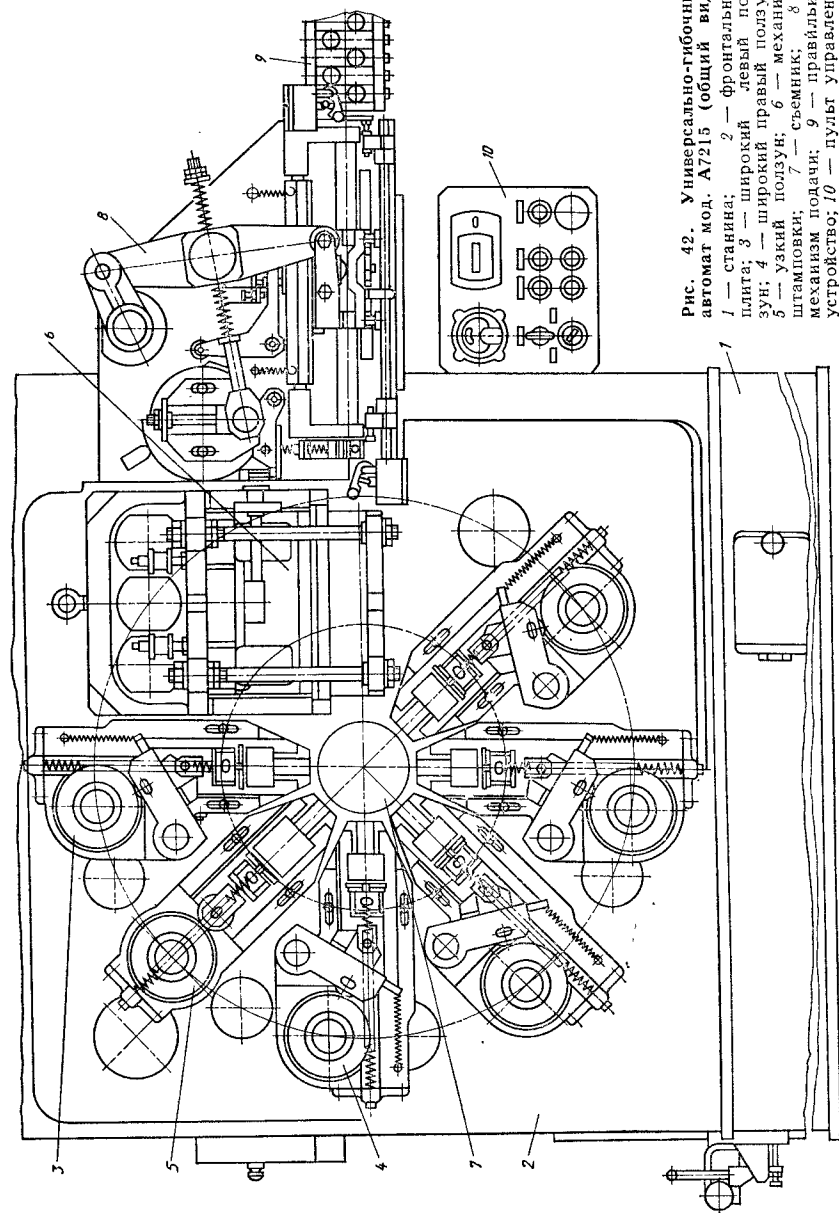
Универсально-гибочный автомат мод. А7215 (общий вид): 1 — станина; 2 — фронтальная плита; 3 — широкий левый ползун; 4 — широкий правый ползун; 5 — узкий ползун; 6 — механизм штамповки; 7 — сьемник; 8 — механизм подачи; 9 — правяльное устройство; 10 — пульт управления
